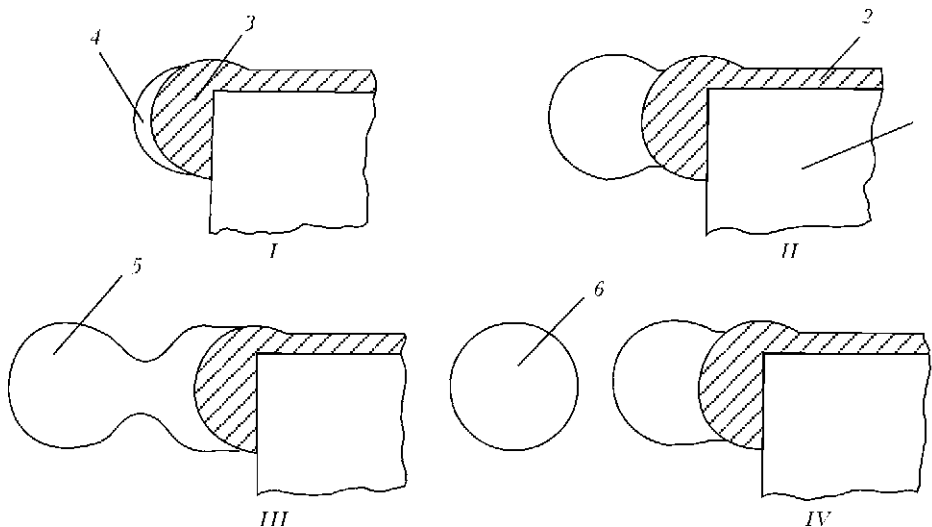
Схемы каплеобразования (I–IV): 1 — заготовка; 2 — слой жидкого металла; 3 — кольцо; 4 — образующийся мениск; 5 — отрывающаяся капля; 6 — гранула
